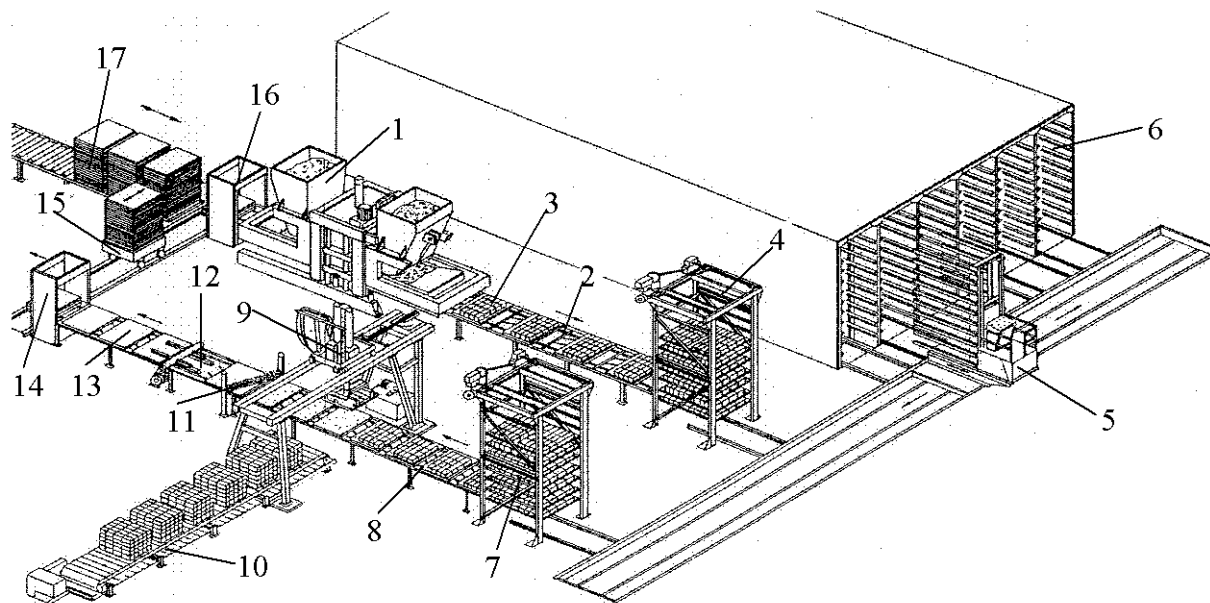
Схема конвеєрної лінії з камерою тверднення фірми "KNAUER": 1 — формувальна установка (стаціонарний вібропрес); 2 — формувальний конвеєр; 3 — піддони з виробами; 4 — пакувальник виробів на піддонах; 5 — машина для встановлення і виймання пакету виробів на піддонах в камери дозрівання; 6 — камера дозрівання (ТВО за рахунок екзотерії цементу); 7 — установка для розбирання пакету; 8 — конвеєр розпалублення і підготовки піддонів; 9 — штабелювальник (машина для знімання виробів з піддонів і створення транспортних пакетів); 10 — конвеєр створення транспортних пакетів; 11 — пристрій для очищення піддонів; 12 — пристрій для змащення піддонів; 13 — піддони; 14 — машина для складання піддонів в стопи; 15 — візок для переміщення піддонів до конвеєру формування; 16 — машина для розбирання стопи піддонів і подавання їх під прес; 17 — конвеєр зберігання стоп піддонів.
